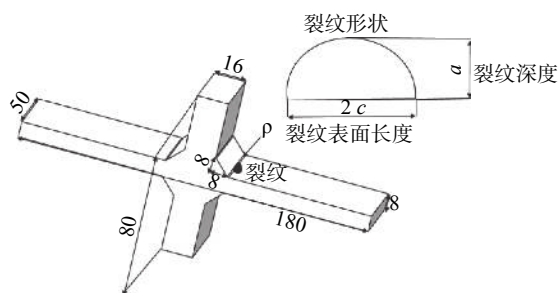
十字焊接接头及裂纹几何参数 (mm)
